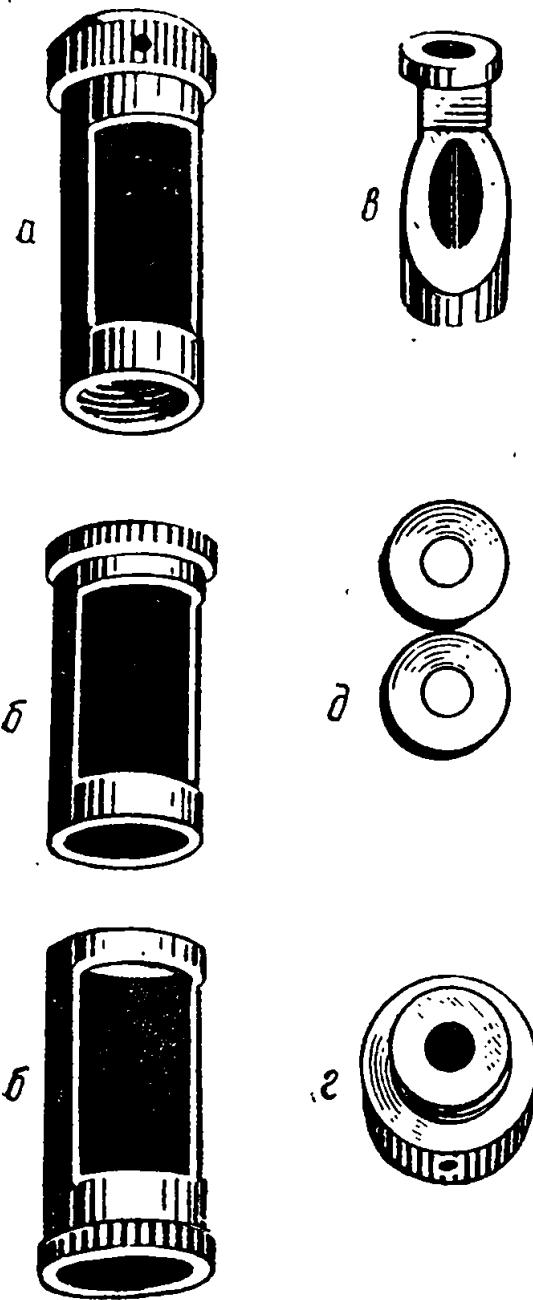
Компенсатор в разобранном виде: *а* — корпус; *б* — регуляторы разных диаметров; *в* — дульный тормоз; *г* — соединительная гайка; *д* — тарельчатые пружины
